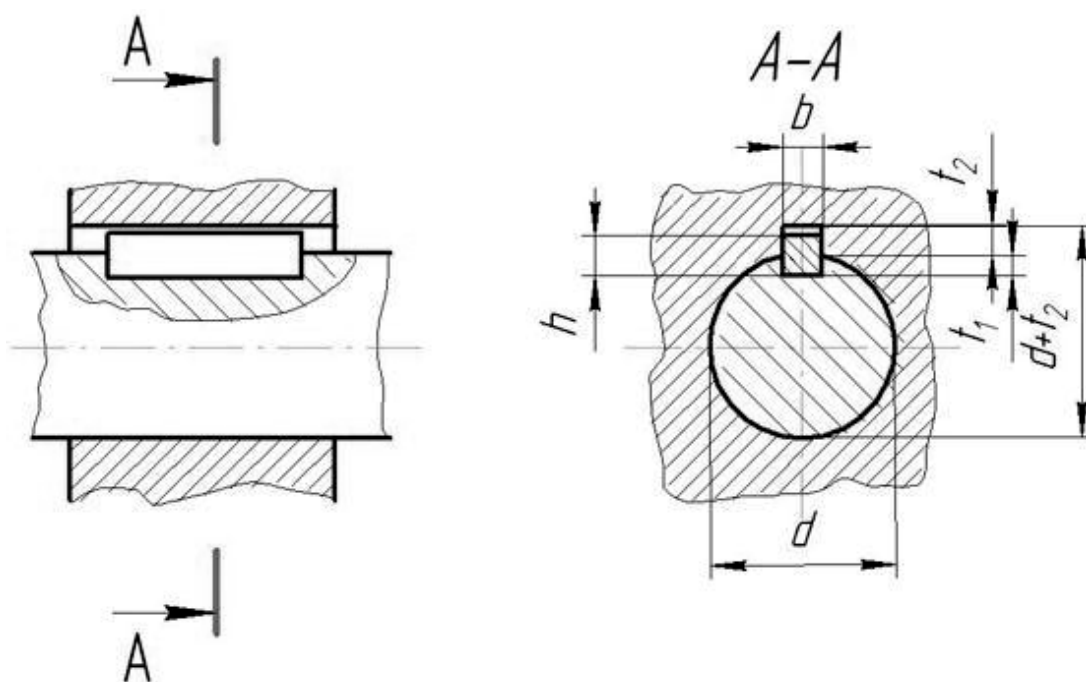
Постановка размеров деталей шпоночного соединения
